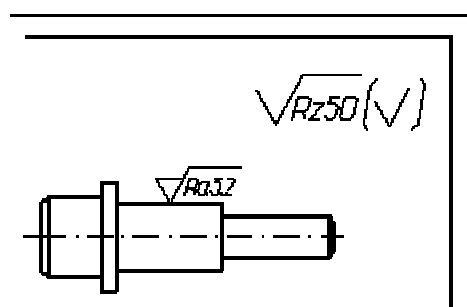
Указание шероховатости одинаковой для части поверхностей изделия
